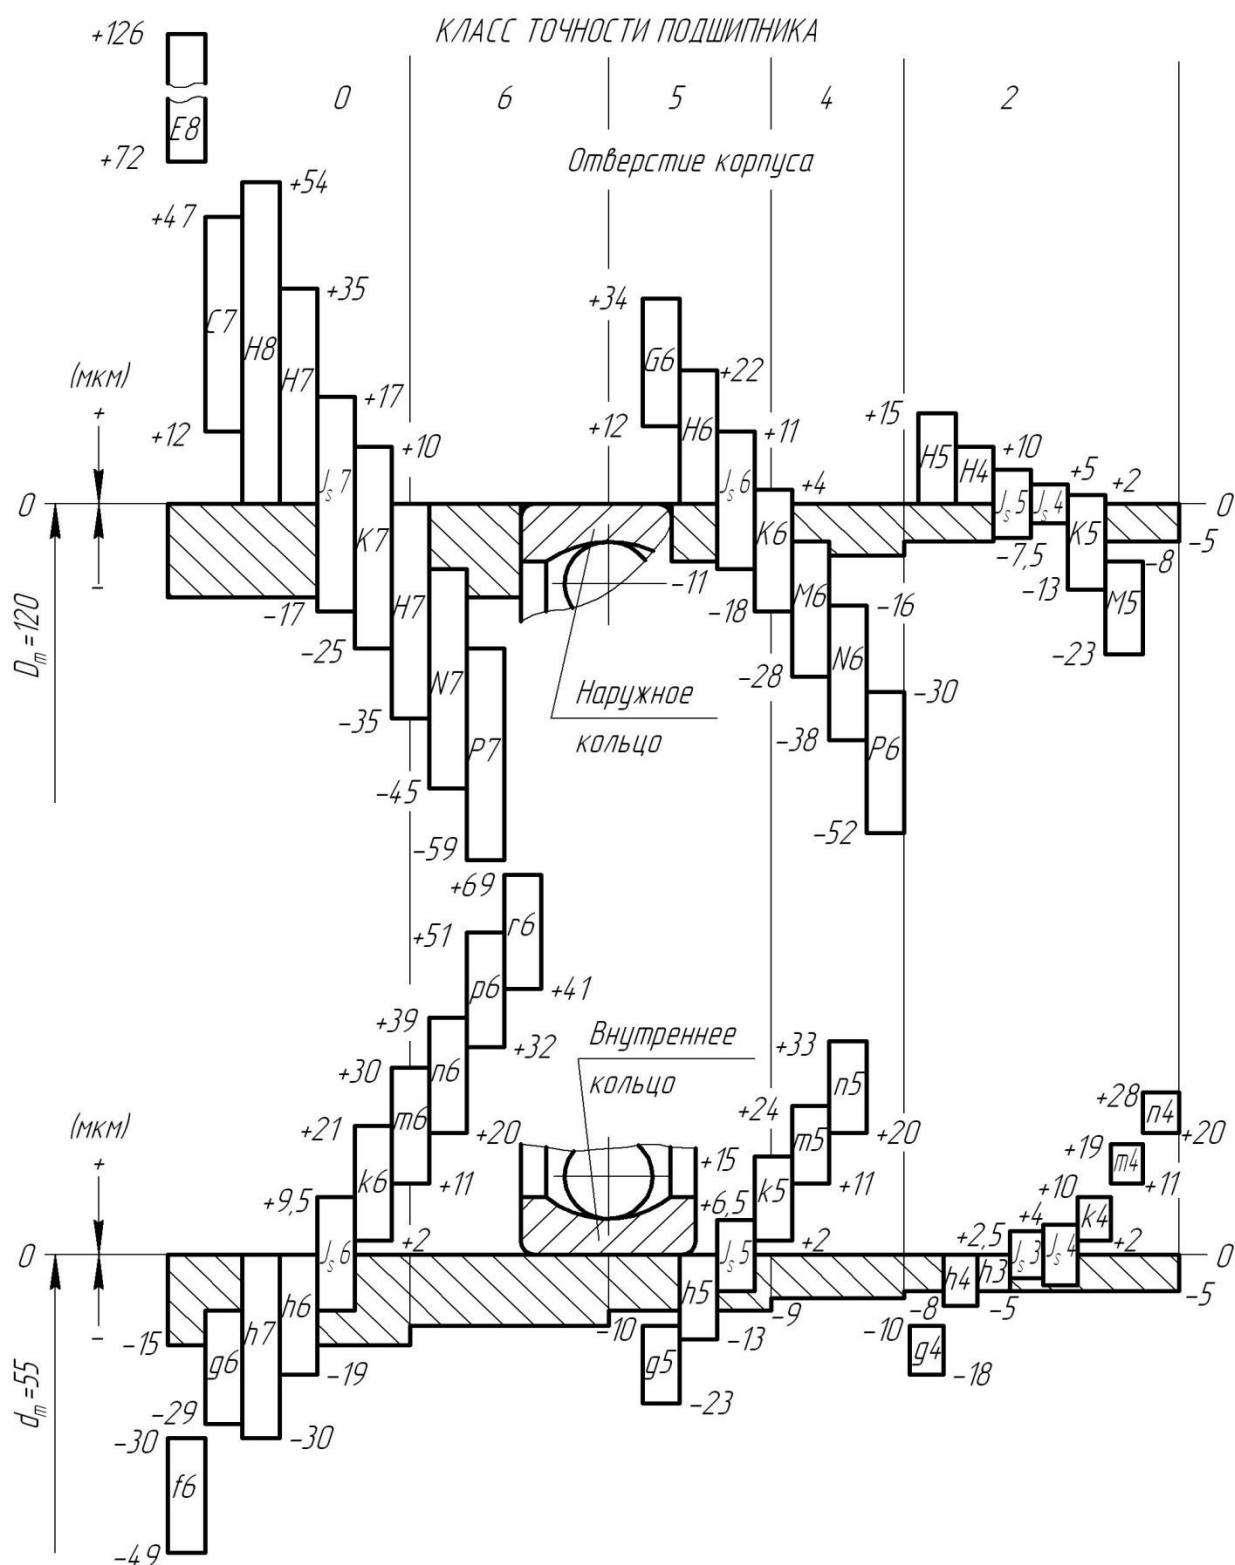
Схема расположения полей допусков на диаметры колец подшипников качения (*KB*- внутреннего; *hB*- наружного), отверстий в корпусах и валов (отклонения в мкм).
